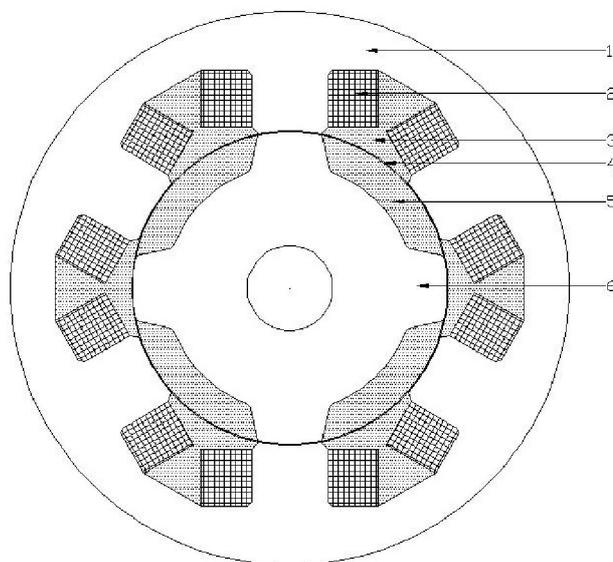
Активная часть ВИМ: 1 – магнитопровод статора; 2 – обмотка статора; 3 и 5 – твердый диэлектрический и неферромагнитный материал, расположенный соответственно на статоре и роторе; 4 – зазор между статором и ротором, заполненный МЖ; 6 – магнитопровод ротора.
